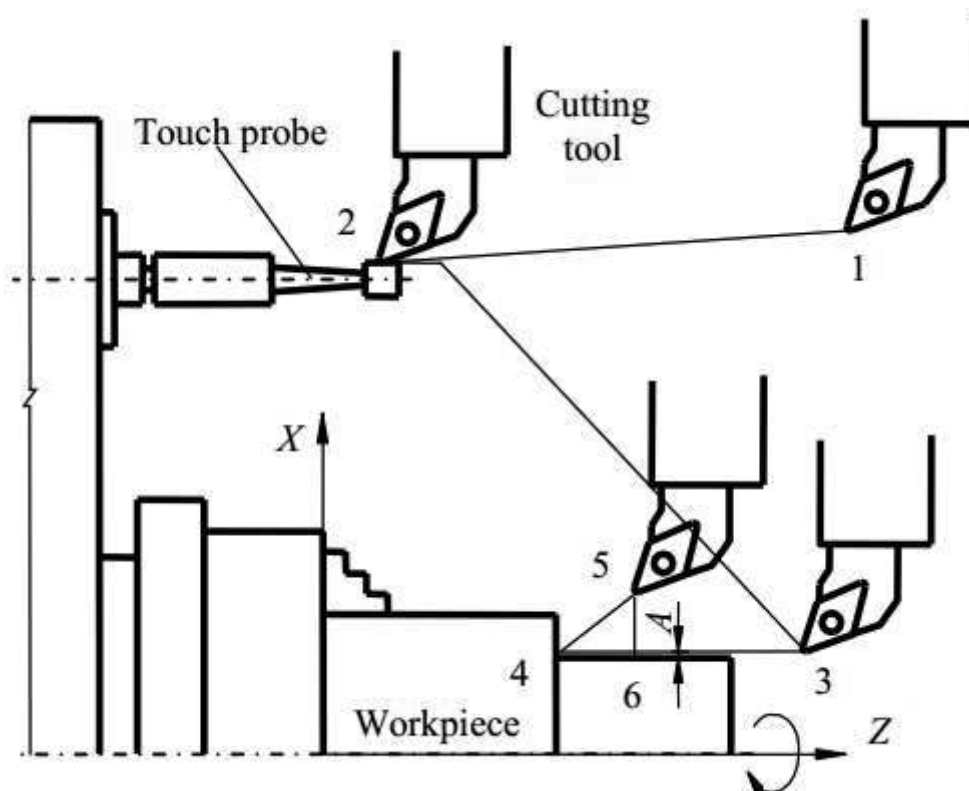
Измерение размера заготовки с помощью режущего инструмента
